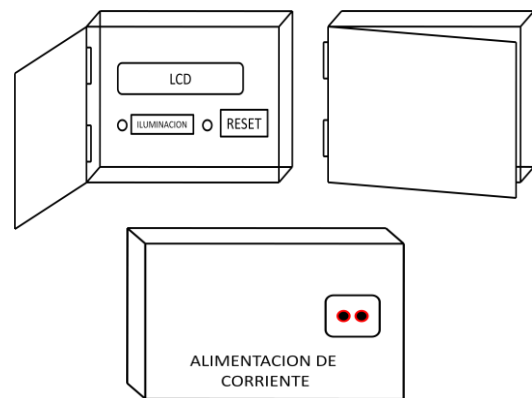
Diseño inicial de la caja protectora. Parte frontal (interna y externa) y posterior
